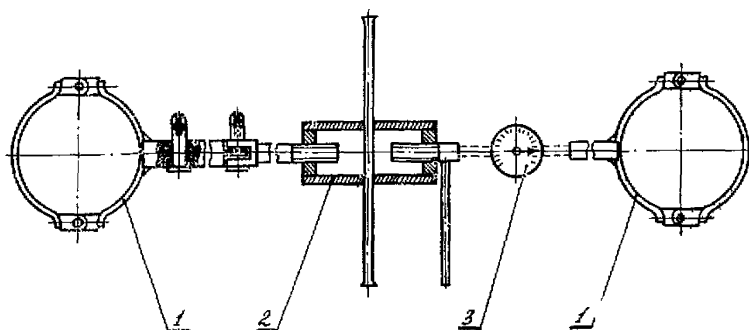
Приспособление П-Г для механических испытаний изоляторов:
